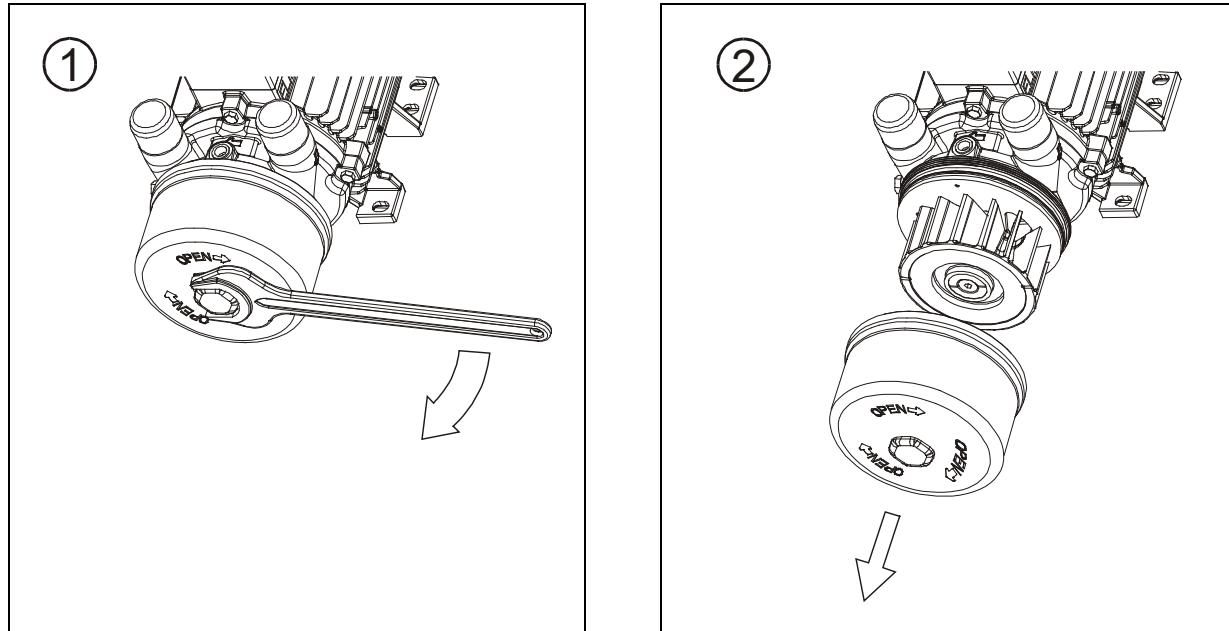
Démontage du corps de la pompe à vide / compresseur
